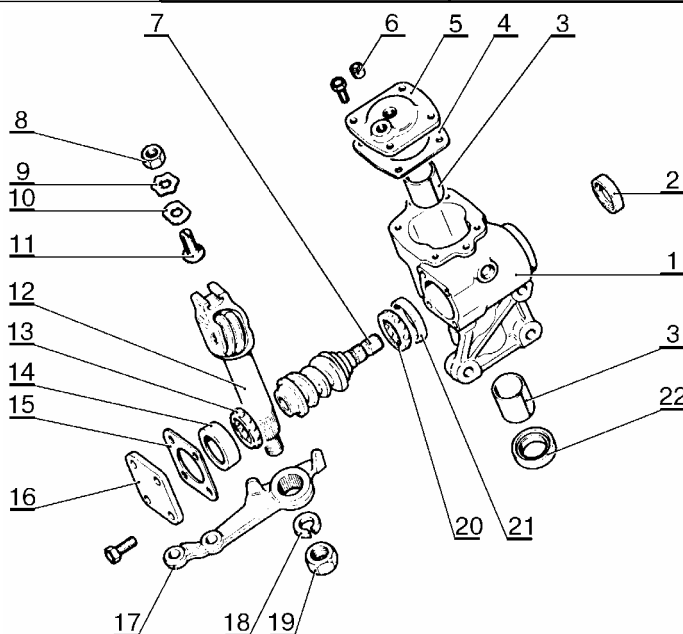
Сборка рулевого механизма 2101/05/21/213-3400010:
